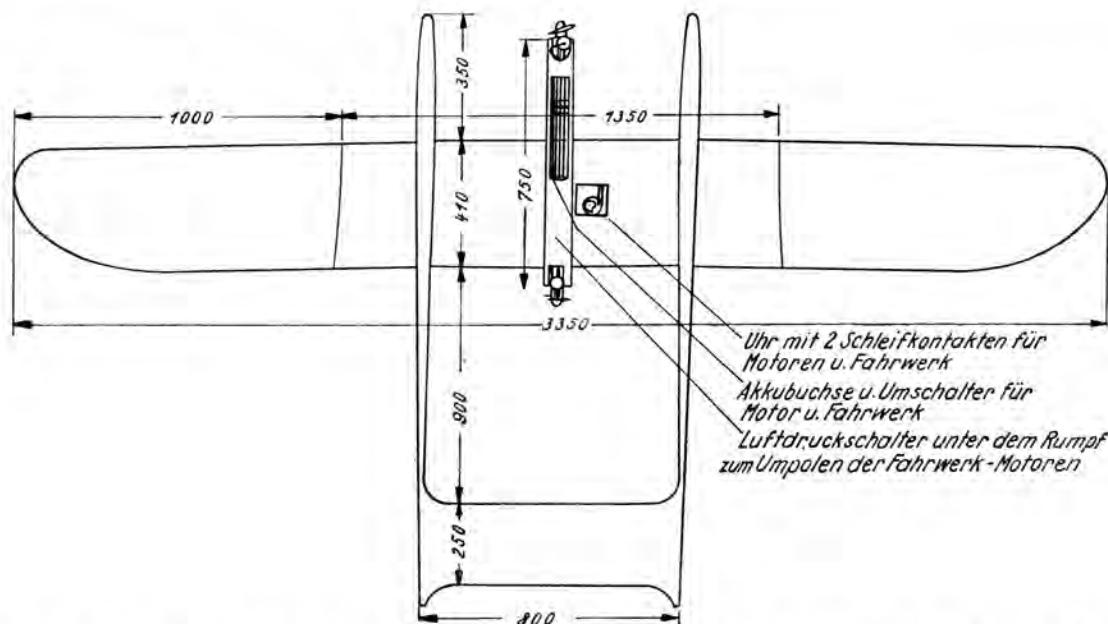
Draufsichtzeichnung des Doppelrumpf-Benzinmotor-Flugmodells zur Veranschaulichung des Einbaues des Triebwerks für die Luftschrauben und das Fahrwerk
